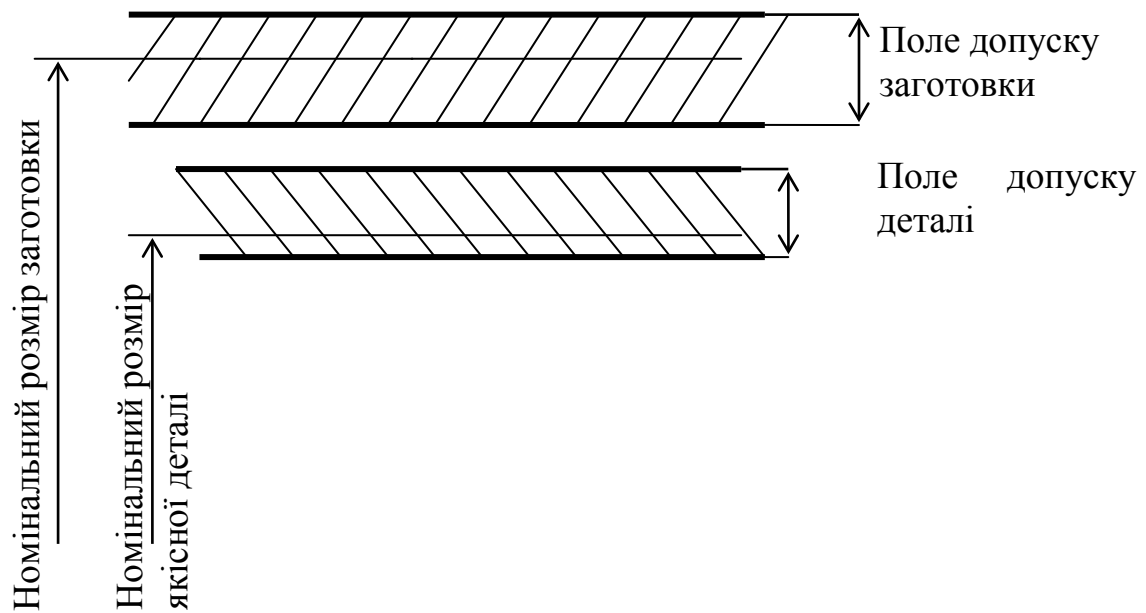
Поле допусків заготовки та деталі
